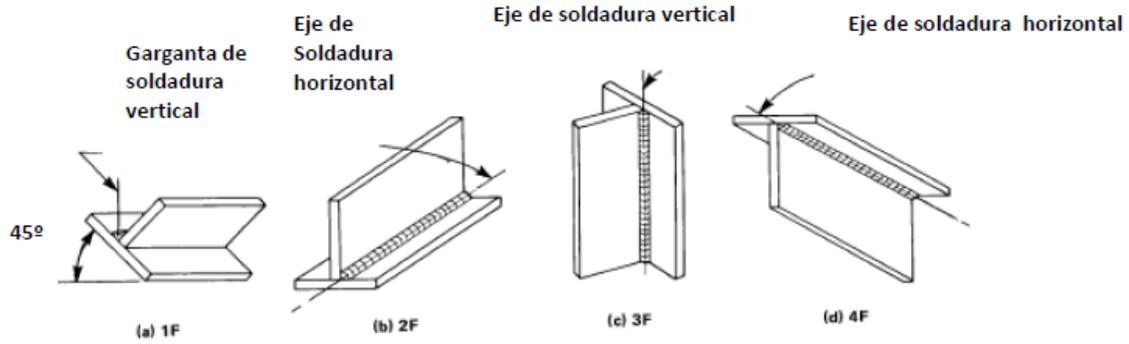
POSICIONES DEL ENSAYO PARA SOLDADURAS DE FILETE.
